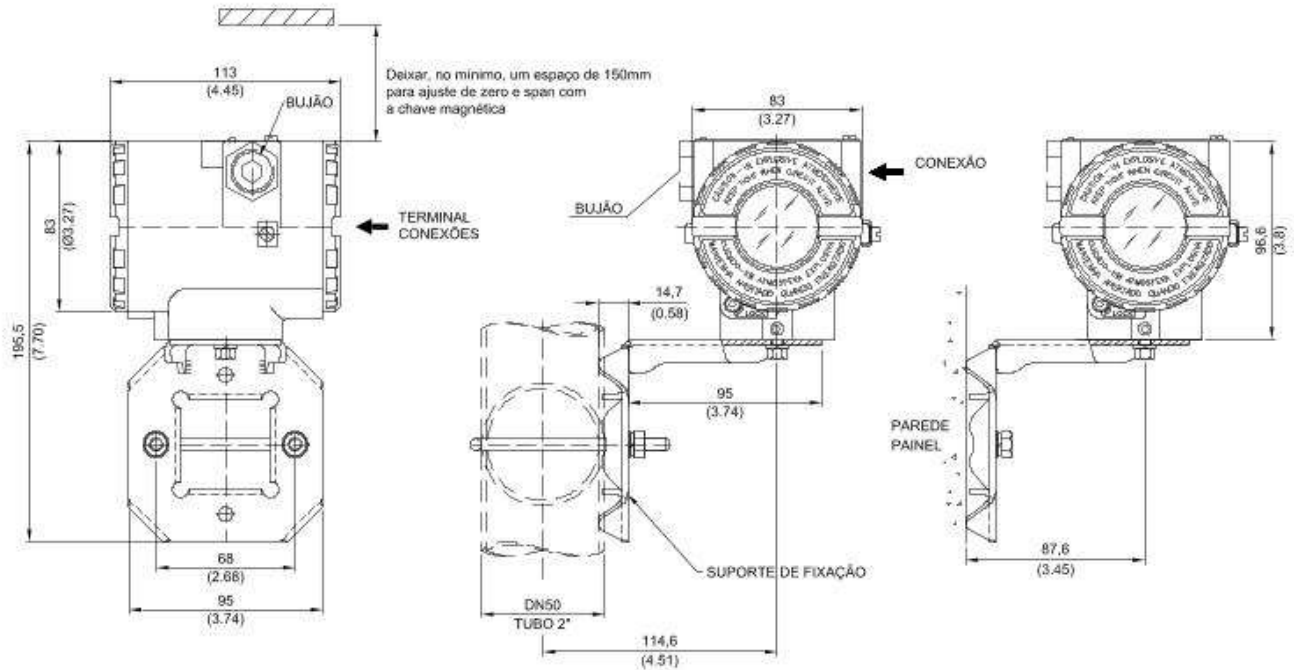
Desenho Dimensional e Posições de Montagem
